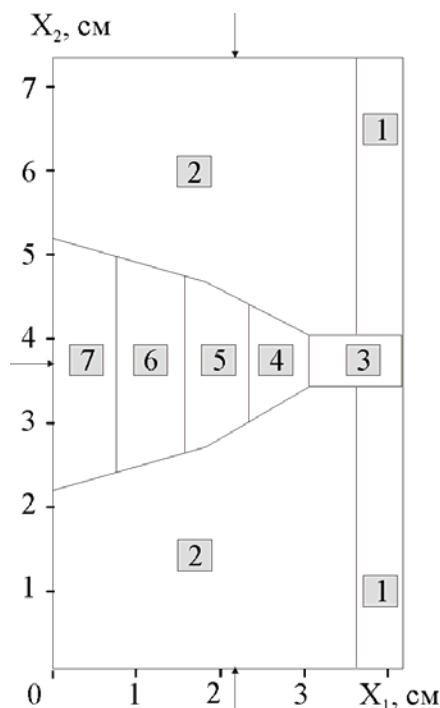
Схема сварного соединения: 1 – плакирующий слой; 2 – основной металл; 3, 4, 5, 6, 7 – слои шва, которые последовательно наносятся при многопроходной сварке
